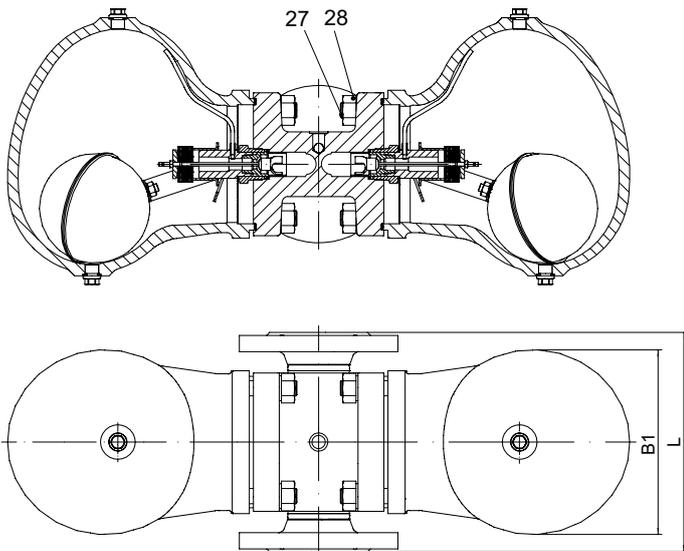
1 mit Flanschen - horizontale Einbaulage
